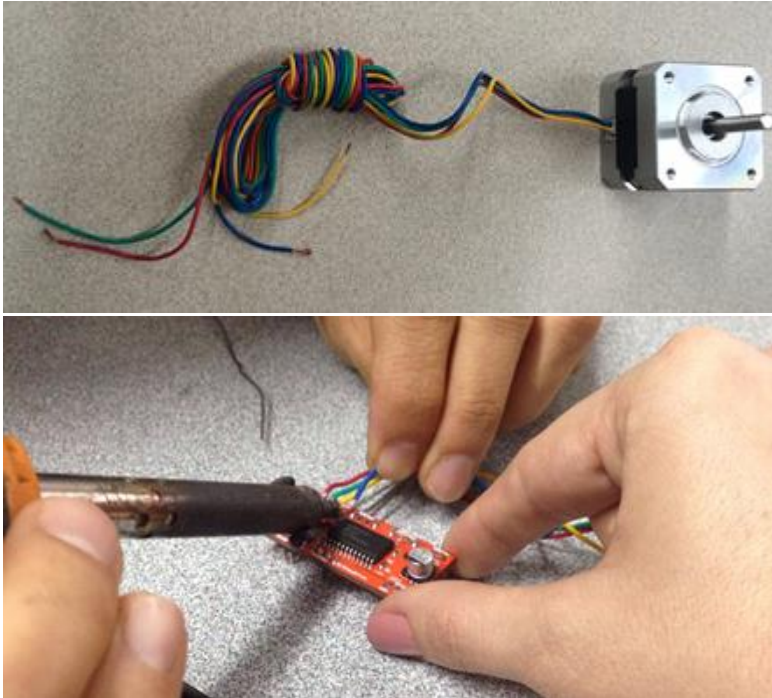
Soldar con cautín los cables del motor de pasos al controlador del motor.
